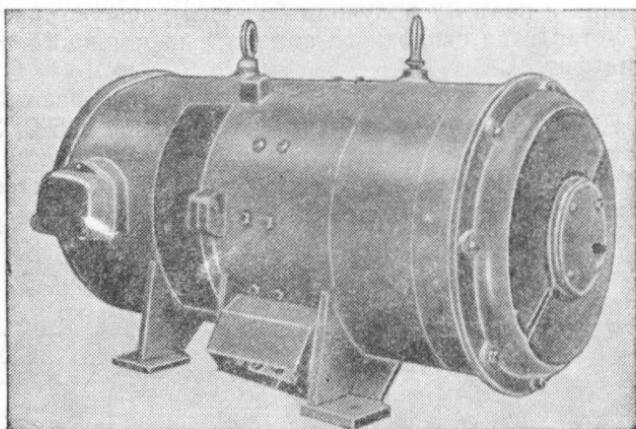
Передвижная сварочная машина постоянного тока типа СУГ-2р:
